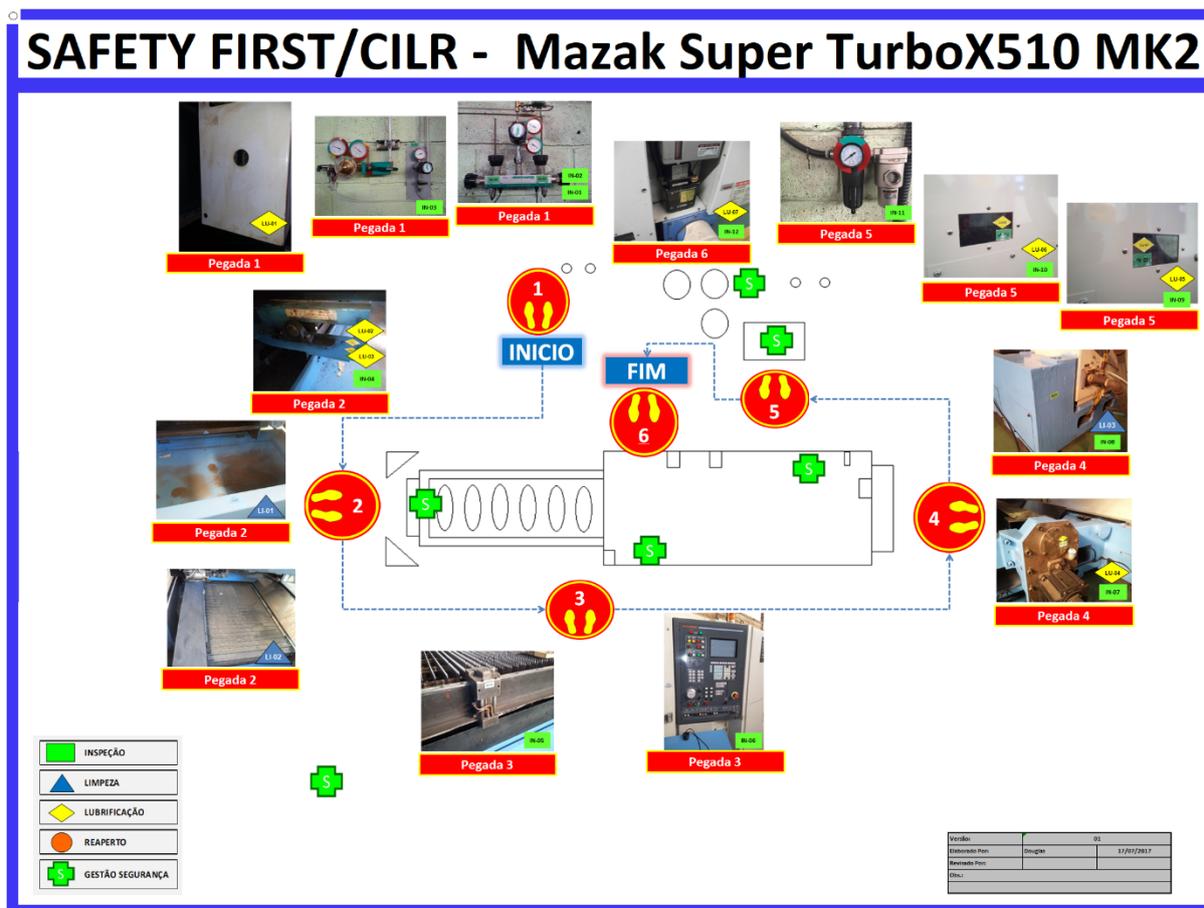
Depois - Máquina Mazak Super Turbo.
